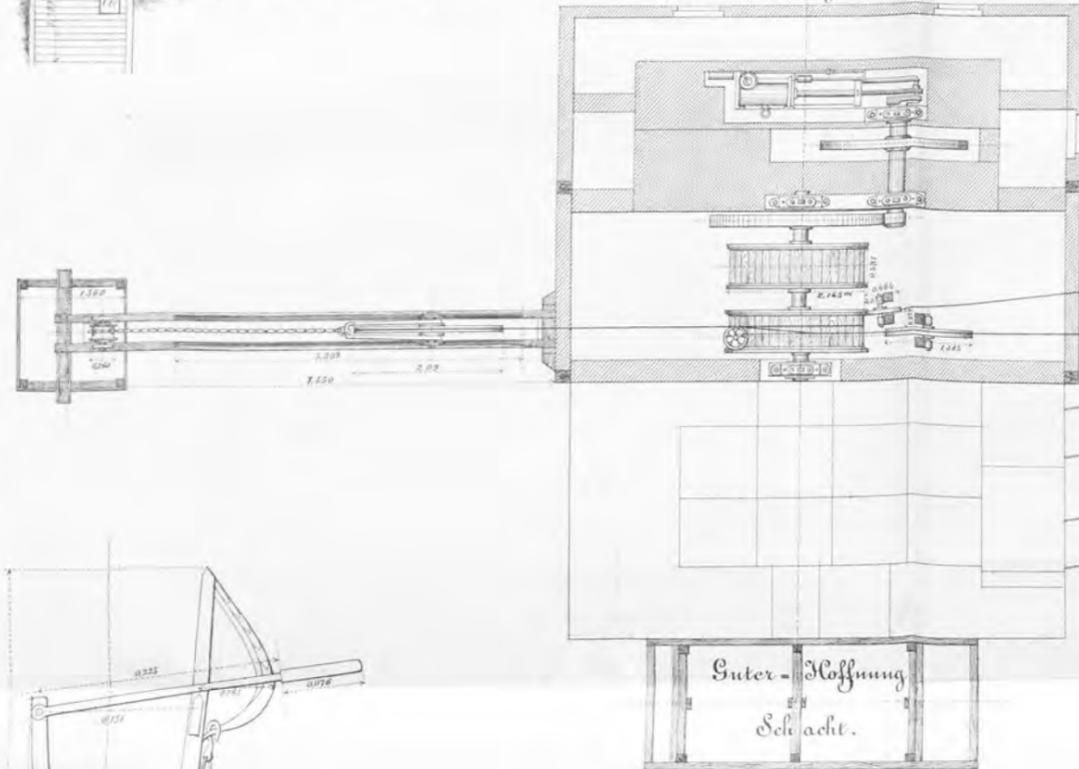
Grundriss  $\frac{1}{12}$  nat. Gr.
